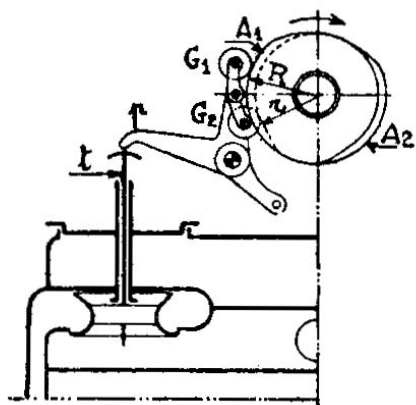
Posición I. – Admisión cerrada, pero a punto de abrirse
